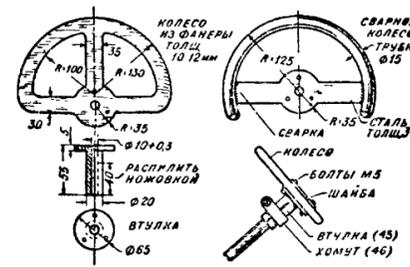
Рулевое колесо и его крепление на рулевом валу. Втулка выпиливается из стали 35 и крепится к рулевому колесу тремя болтами М5, хомут изготавливается из стали 20 (ширина 15, толщина 2 мм)
